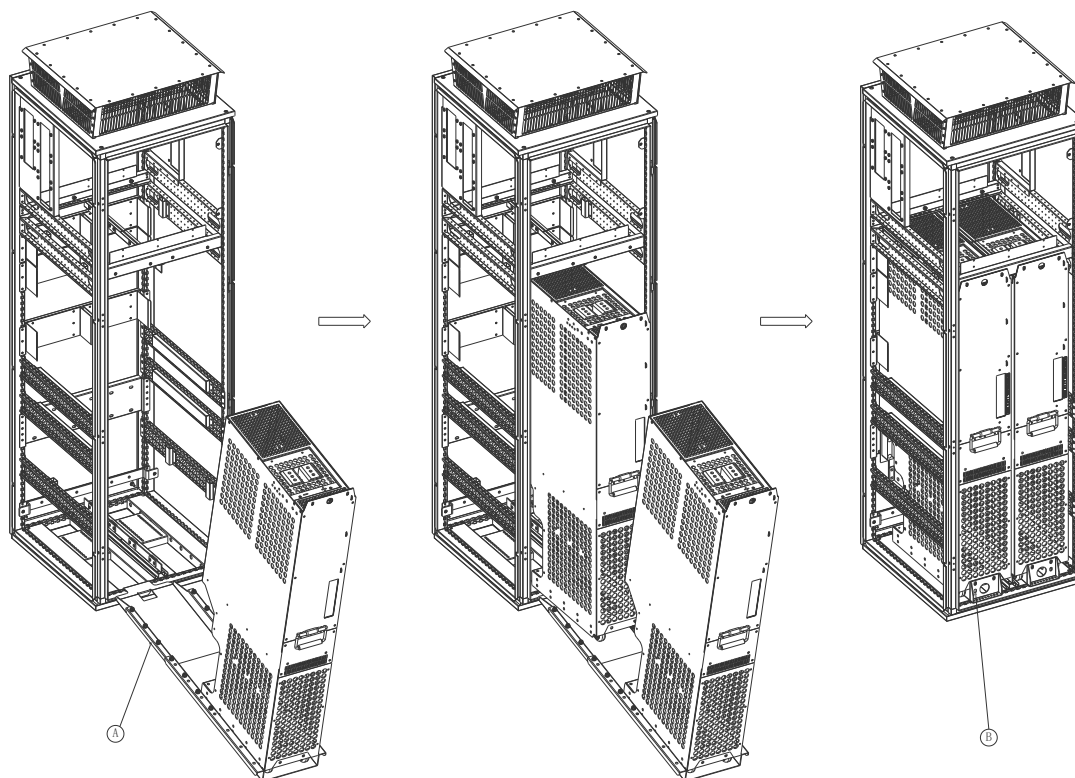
Схема последовательности действий по установке модуля корпуса 2FR8
